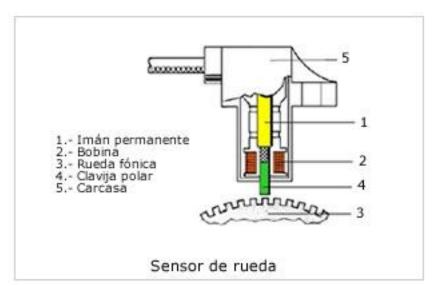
Disposición sensor inductivo sobre rueda delantera
